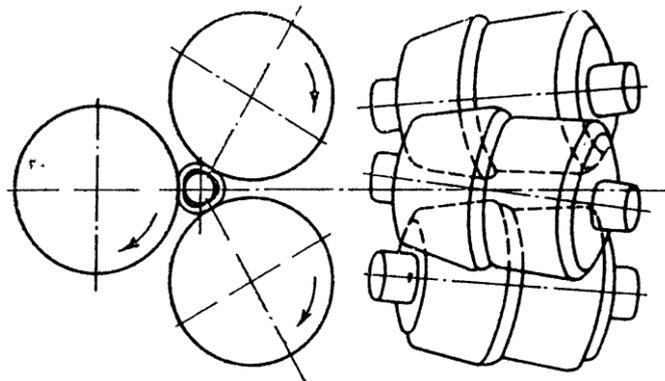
Схема прокатки на трьохвалковому стані
